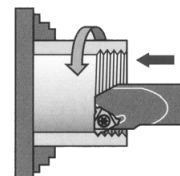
soustružnický nůž pro drážkování, odřezávání a řezání
